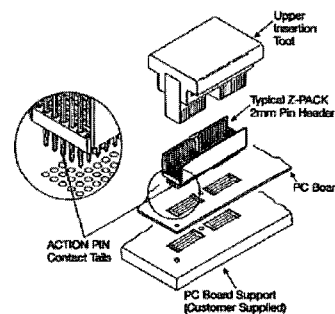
기계적 압력에 의한 PCB 커넥터 삽입.
